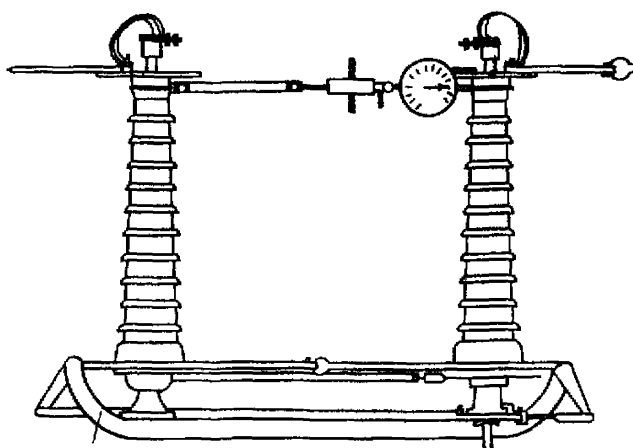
Общий вид полюса отделителя с приспособлением П-1 для механических испытаний изоляторов
